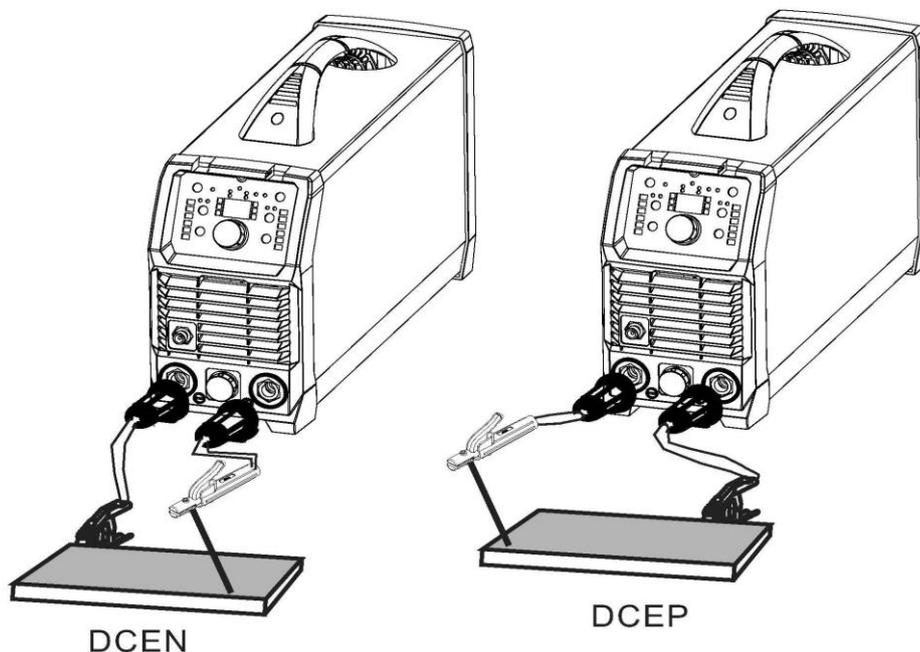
Conexão para soldagem com Eletrodo Revestido.
